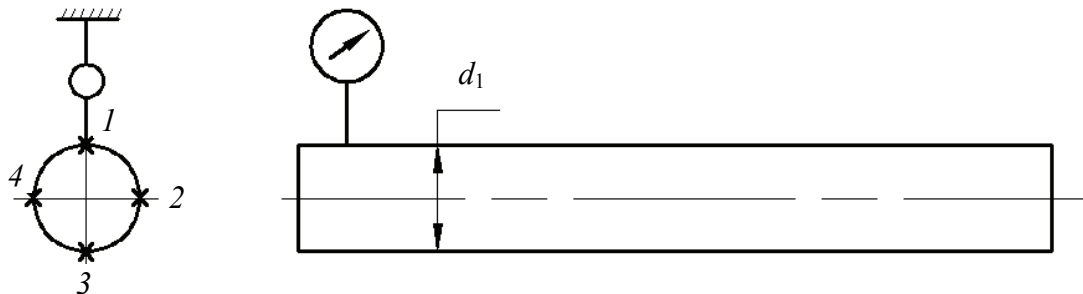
Схема проверки отклонения формы поверхности вала
